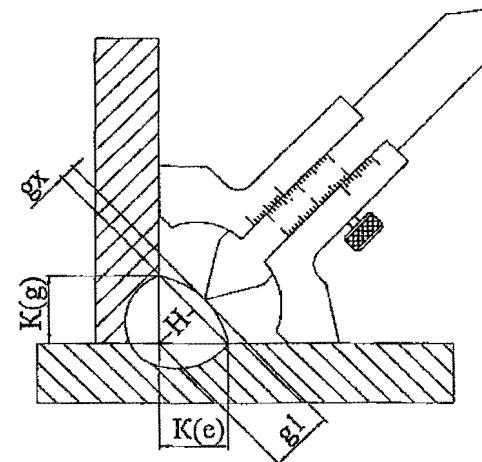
11. Измерение катета шва (К) углового сварного соединения
